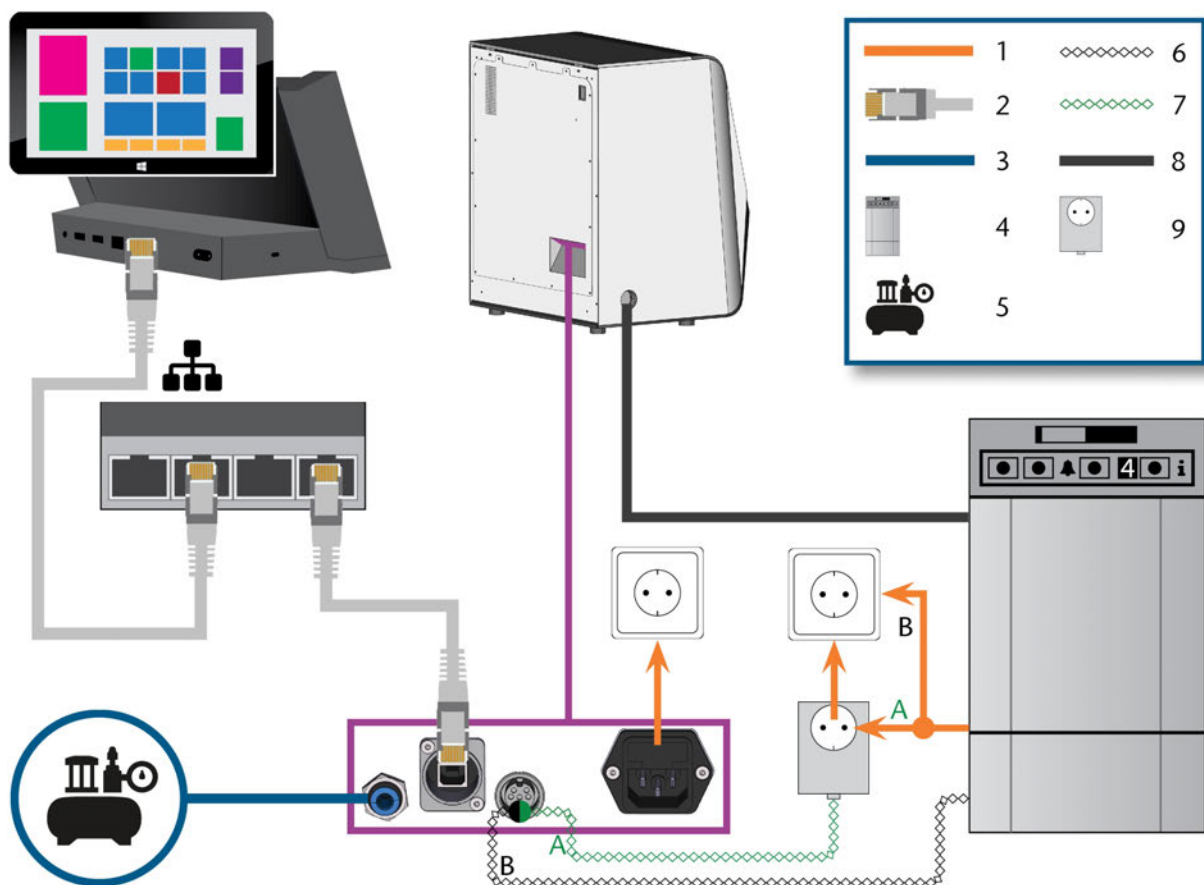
INSTALLATION DE LA MACHINE (SCHÉMA)
